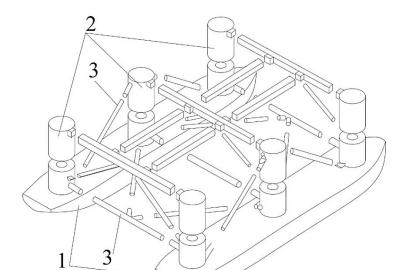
Разбивка конструкций ППБУ на сборочно-монтажные единицы (нижняя часть): 1 — нижние понтоны; 2 — стабилизирующие колонны; 3 — трубчатые связи
